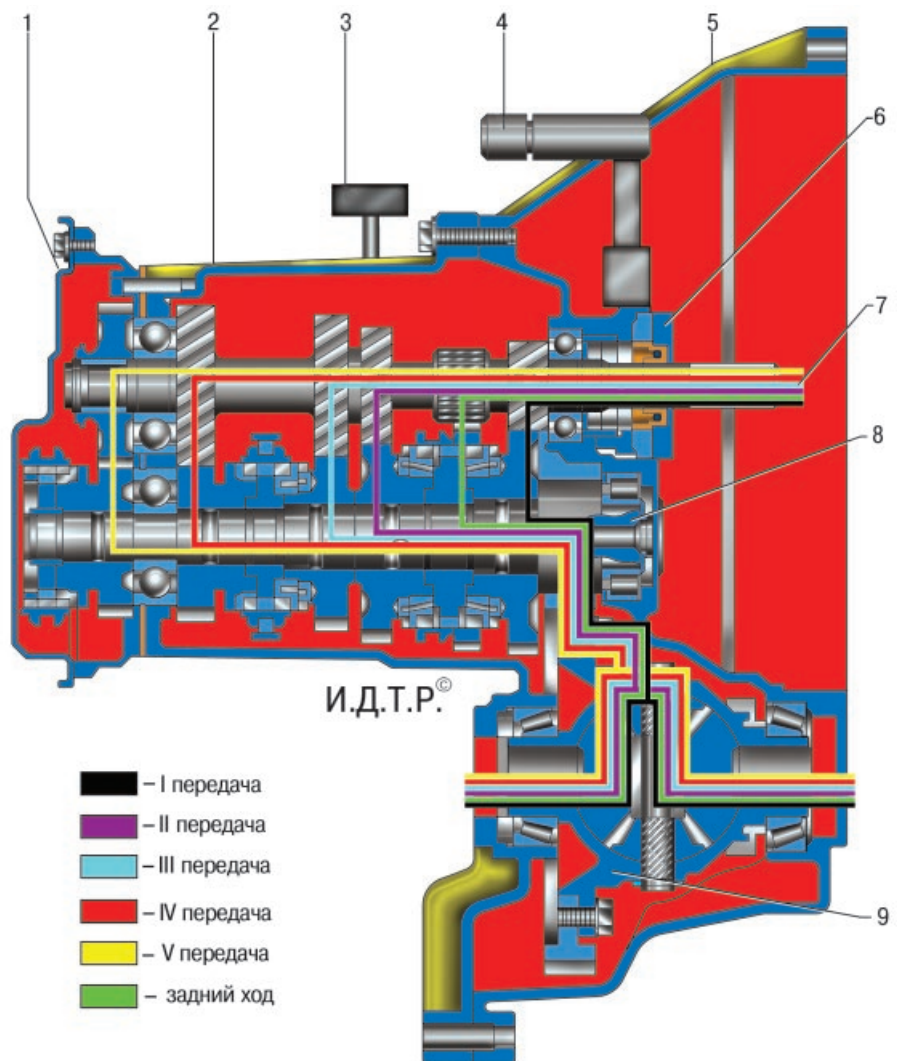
Принципиальная схема пятиступенчатой механической коробки передач: 1 – задняя крышка картера коробки передач; 2 – картер коробки передач; 3 – салун; 4 – рабочий цилиндр гидропривода выключения сцепления; 5 – картер сцепления; 6 – подшипник выключения сцепления; 7 – первичный вал; 8 – вторичный вал; 9 – главная передача и дифференциал
